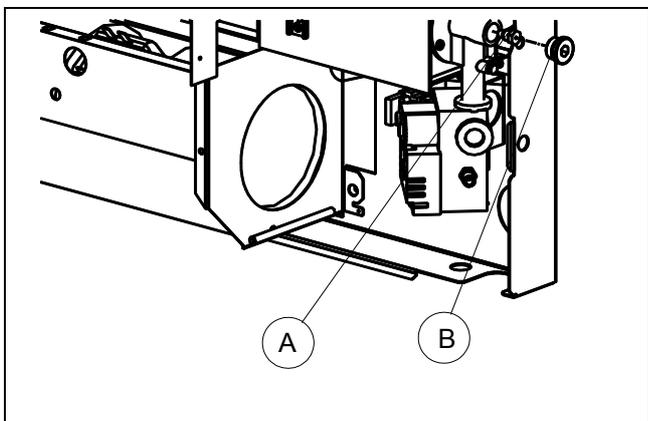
ДЕТАЛЬ БЛОКА ГОРЕЛКИ
